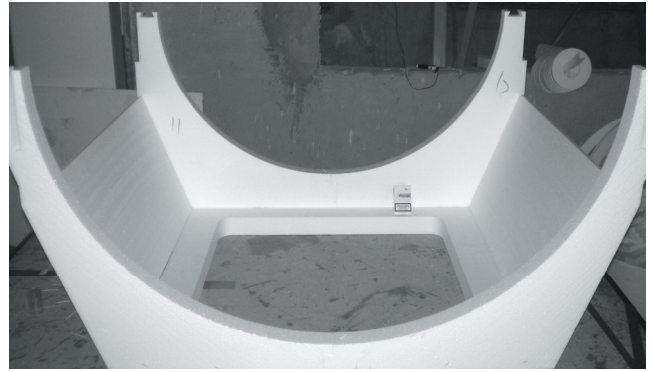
3D-образ пенополистироловой модели литой заготовки корпуса генераторного отсека
